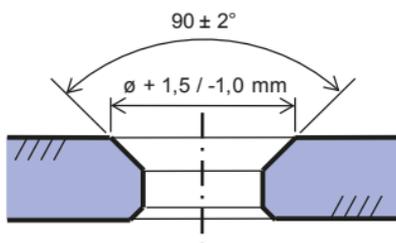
Senklochtoleranzen (\varnothing = Durchmesser)
